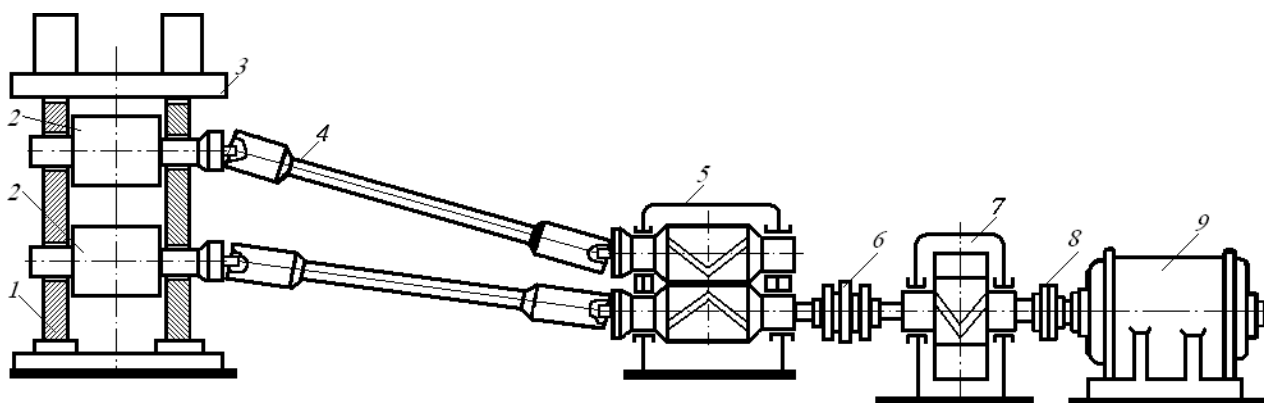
Схема главной линии прокатного стана: 1 – станина; 2 – прокатные валки; 3 – поперечина; 4 – шпиндели; 5 – шестеренная клетка; 6, 8 – муфта; 7 – редуктор; 9 – электродвигатель
